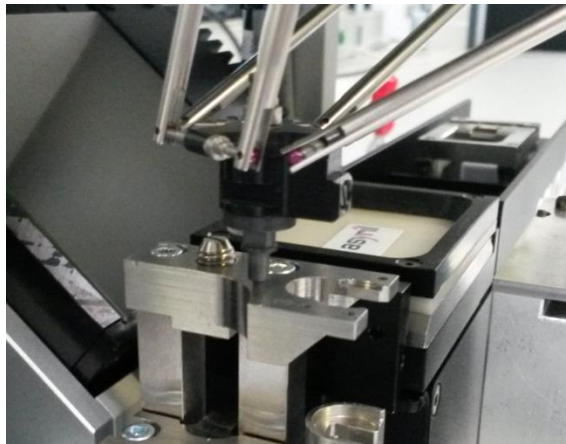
prise de la hauteur outil (avec outil) sur surface plane
